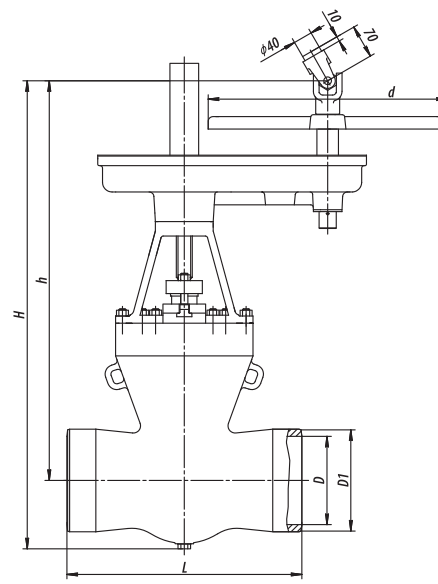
Задвижка DN150...400 с цилиндрическим редуктором
